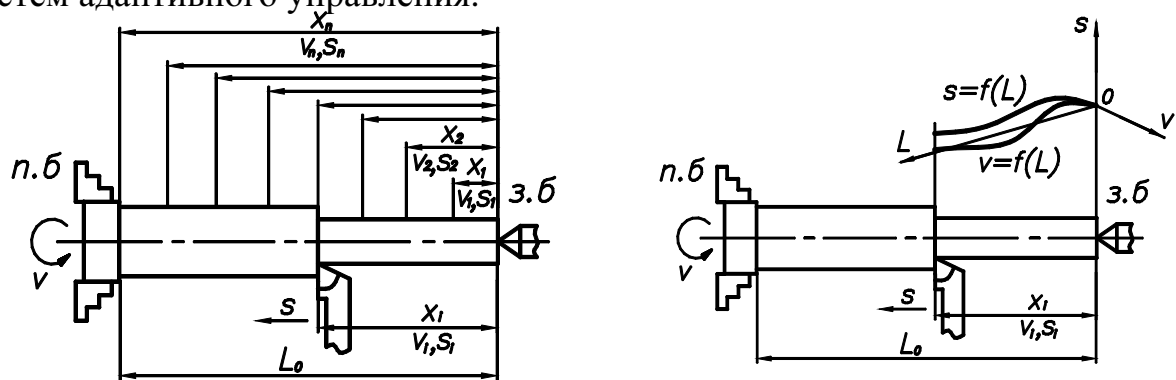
Схемы работы токарных станков с ЧПУ со ступенчатым и бесступенчатым (непрерывным) изменением режимов резания на обрабатываемом участке заготовки
